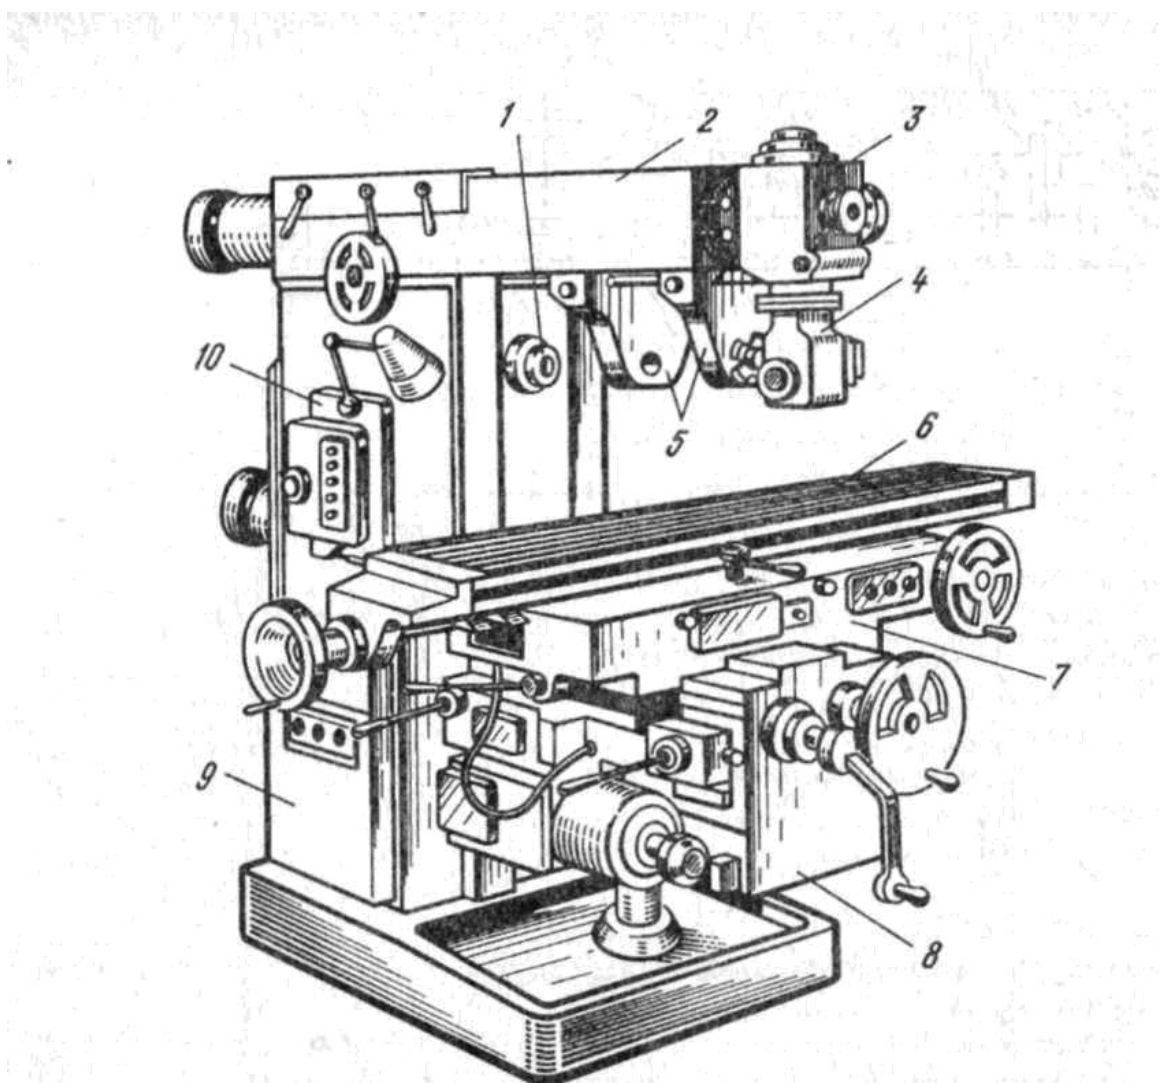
Широкоуниверсальный консольный горизонтально-фрезерный станок.
